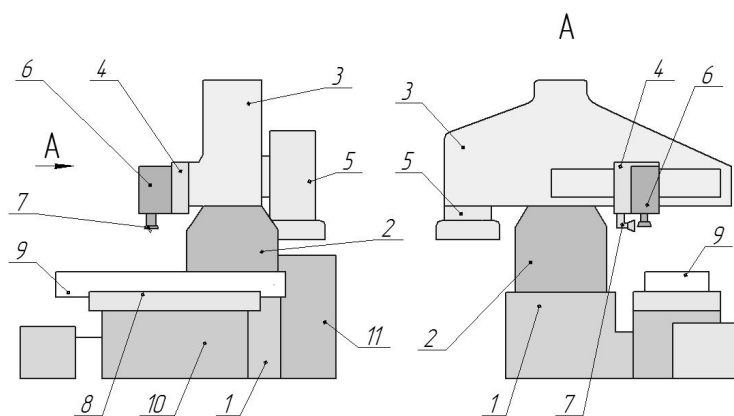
Модернизированный плоскошлифовальный станок 3E711В:
